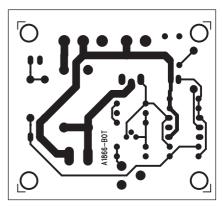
Obrazec desky spojů lineárního regulátoru I (strana TOP)
